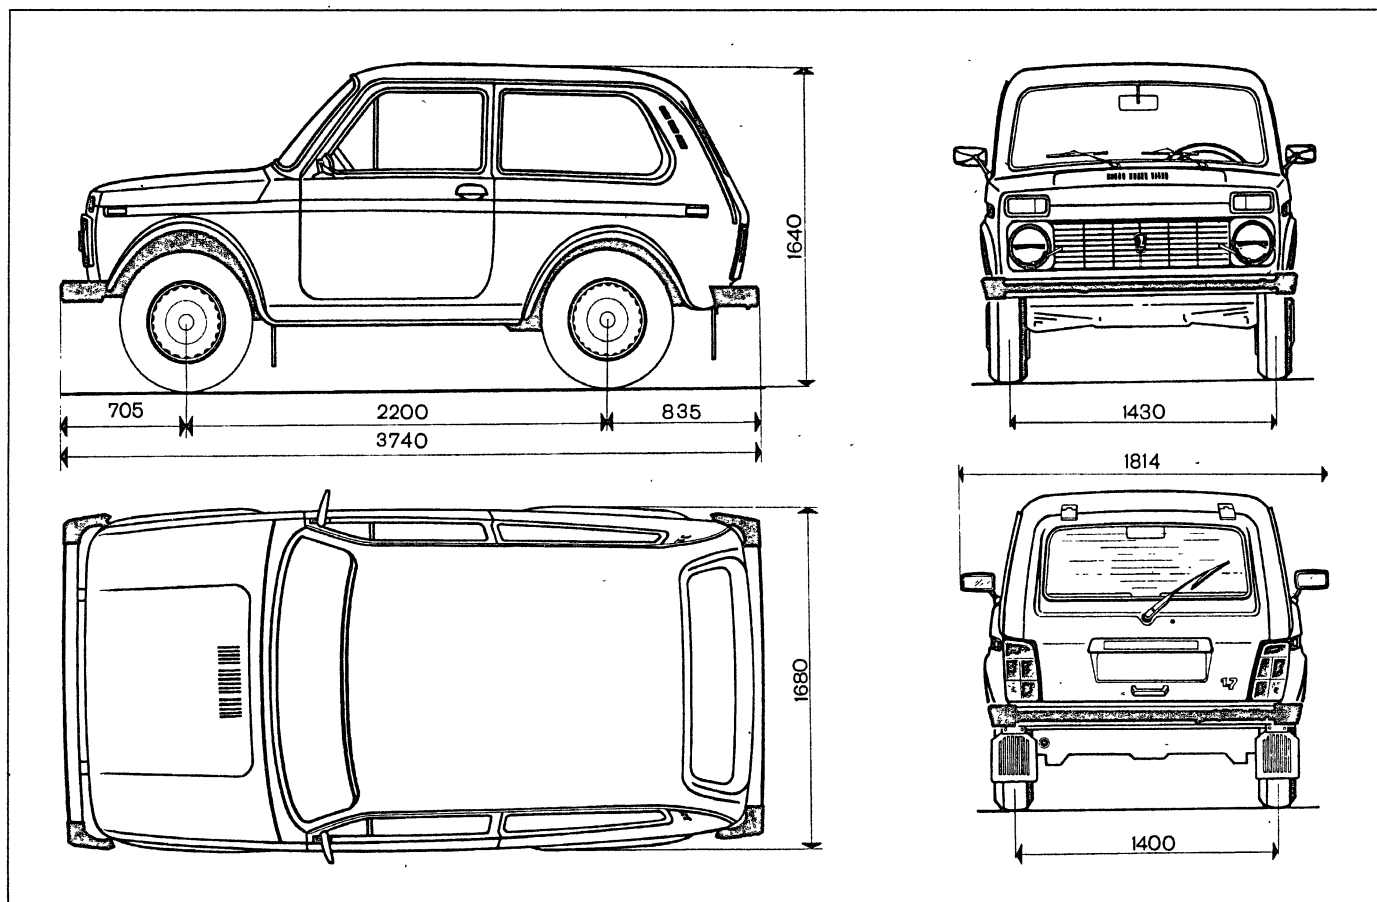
Основные габаритные размеры (справочные) автомобиля ВАЗ-21213
